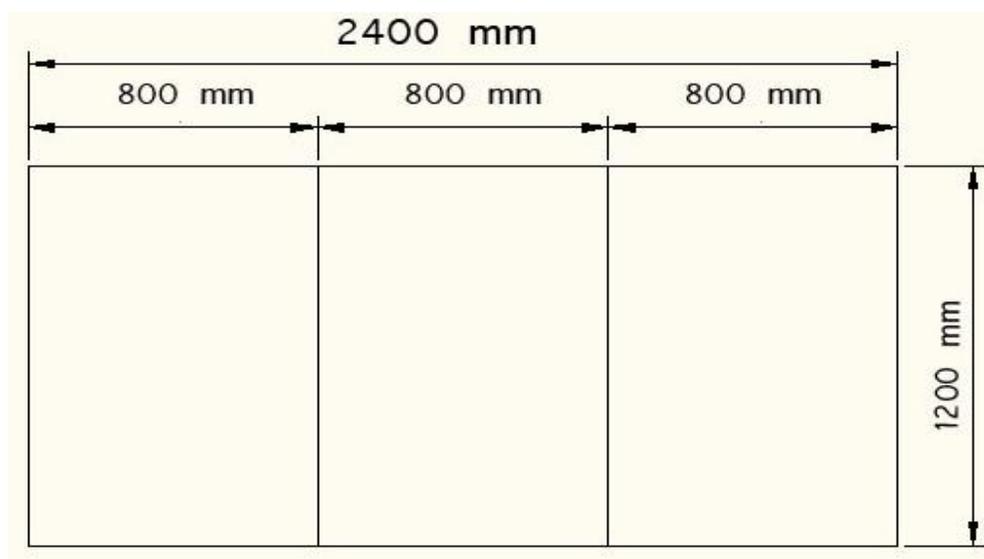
DIVISIÓN DE LA PLANCHA DE ACERO
